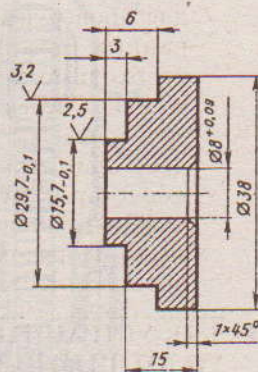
Оправка для запрессовки втулок балансира и противовеса
